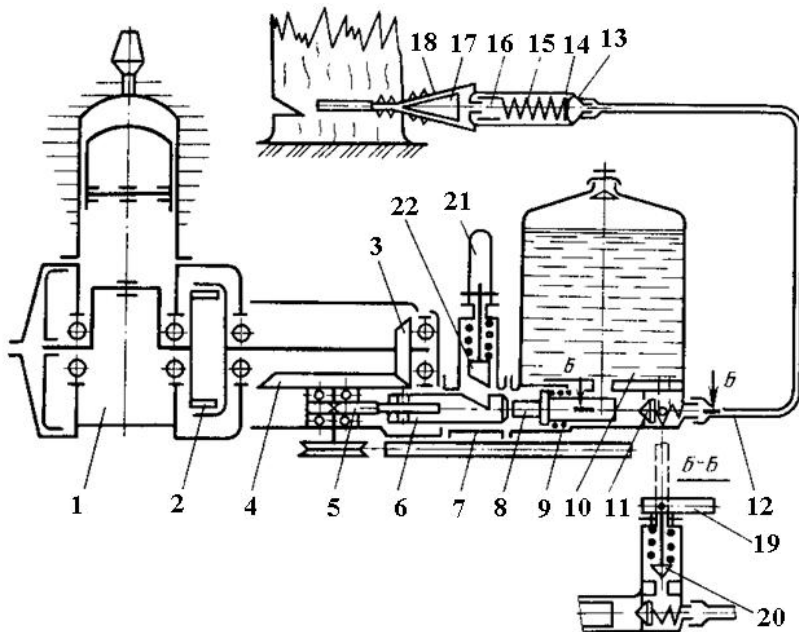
Схема завалювального клина КГМ-1Л [9]:
